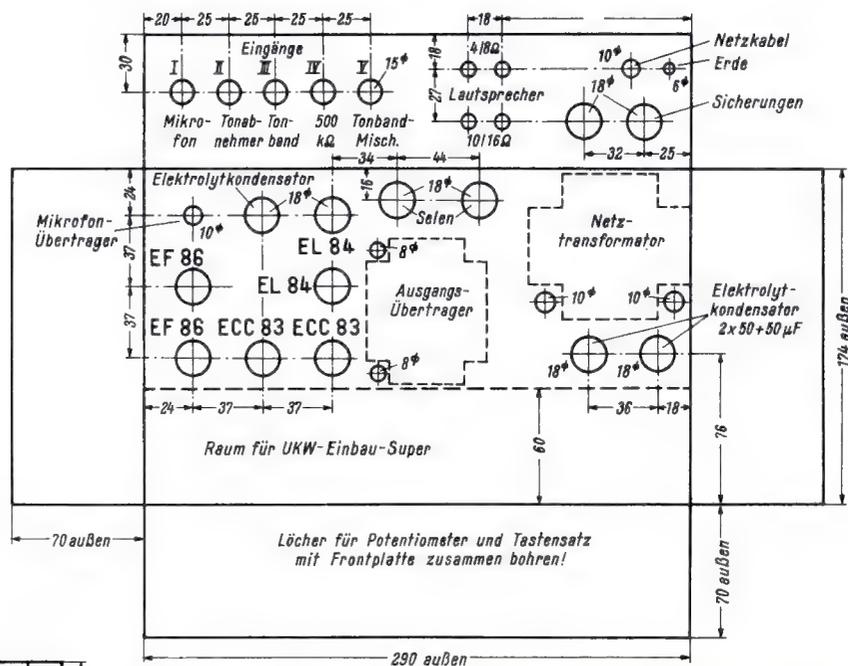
Bohrplan für das Chassis (1 mm Eisenblech, verzinkt)
